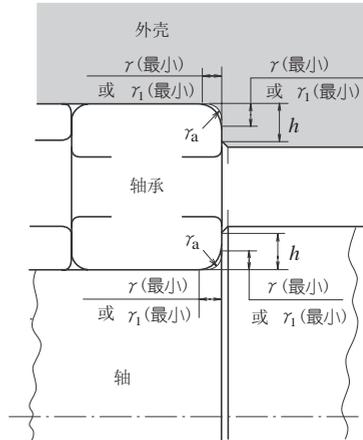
向心轴承的倒角尺寸与轴、轴承座圆角半径与挡肩高度。
